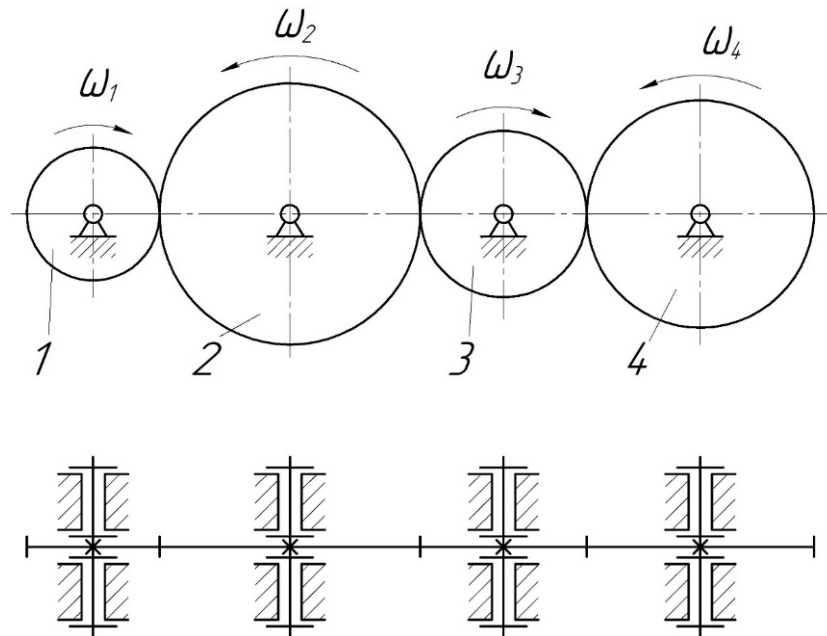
зубчатая передача с последовательным соединением зубчатых колес (рядовая)
